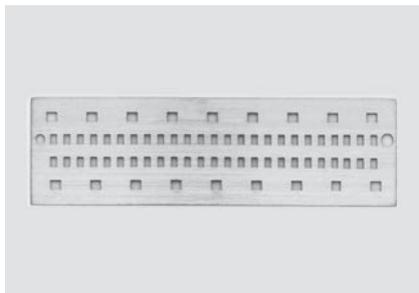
Stecker mit wenig Anschlüssen und einfacher Geometrie
